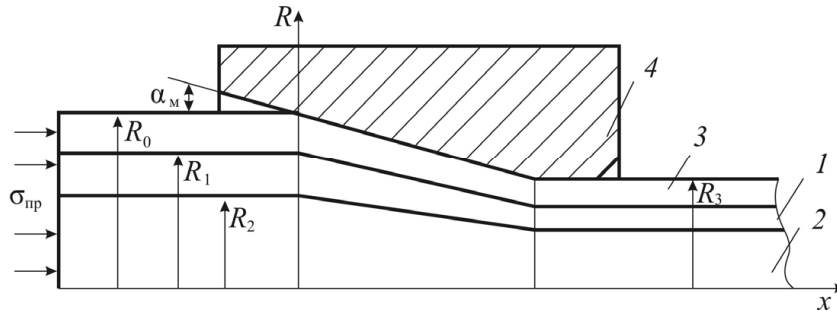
Схема прессования триметаллической сборной заготовки: 1 – промежуточный слой из сверхпроводникового материала (Nb-Ti или Nb); 2 – сердечник из меди; 3 – оболочка; 4 – прессовый инструмент
